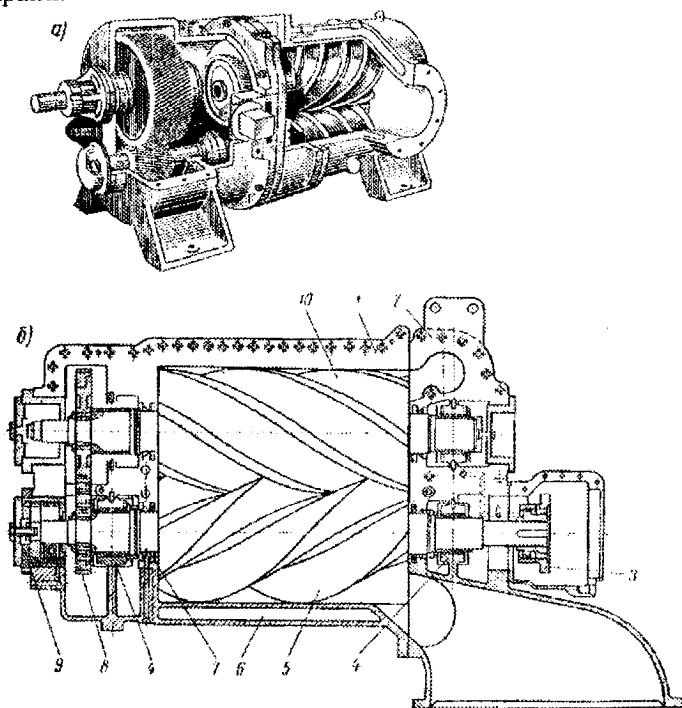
Гвинтовий компресор: а – загальний вигляд; б – розріз; 1 – корпус; 2 – кришка; 3 – муфта; 4 – опорні підшипники; 5 – провідний ротор; 6 – охолоджуюча рубашка; 7 – кільце ущільнювача; 8 – синхронізуючі шестерні; 9 – упорний підшипник; 10 – ведений ротор.
